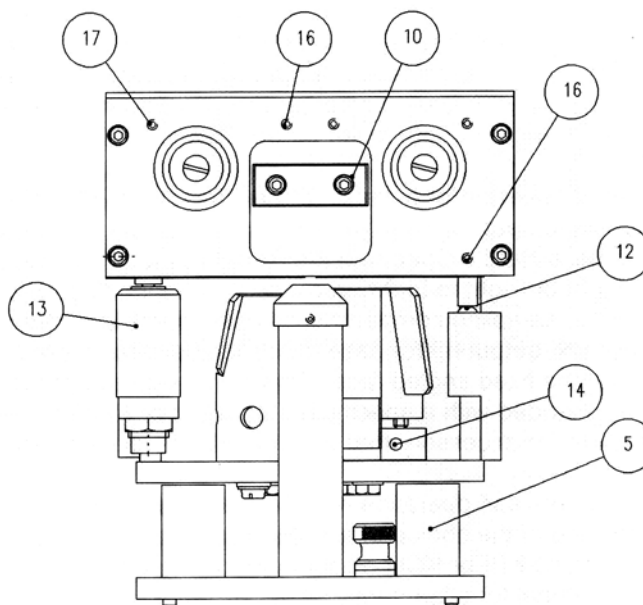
Вид спереди приставки для направления луча слева направо
